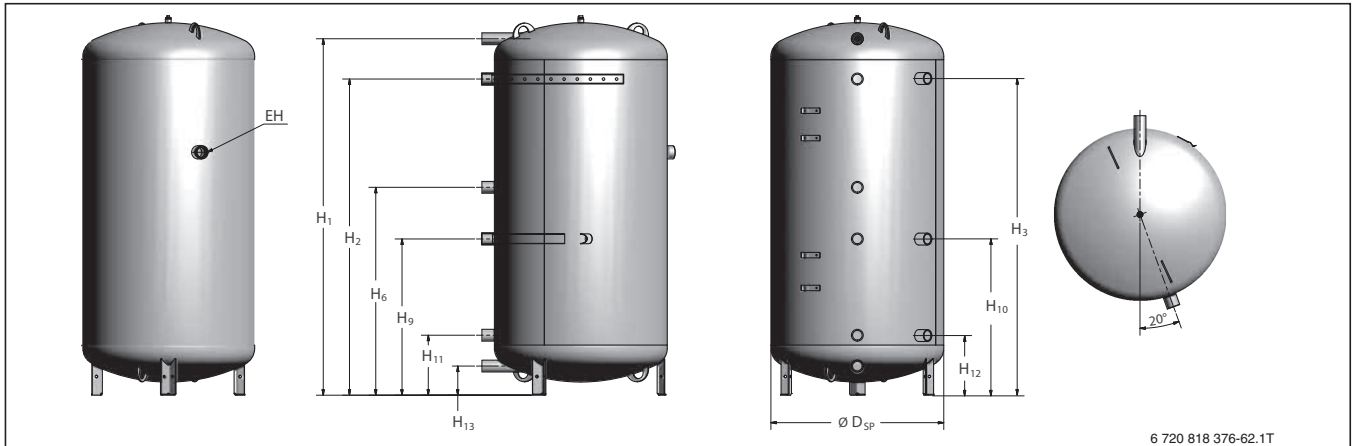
Anschlüsse mit Abmessungen PRZ500/750/1000.6 EW (Darstellung ohne Wärmedämmung)
